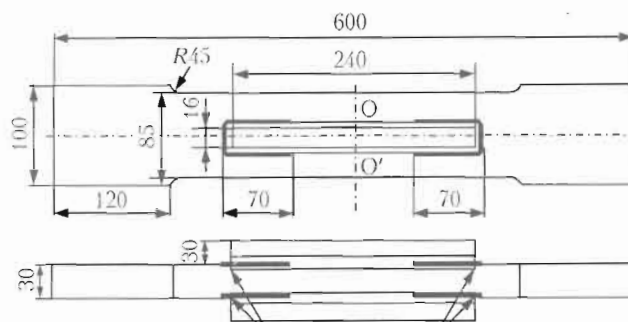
Вид образца для оценки эффективности высокочастотной механической проковки в повышении сопротивления усталости сварных соединений при циклах нагружения простой и сложной формы (стрелками показано расположение зон, обработанных проковкой)
